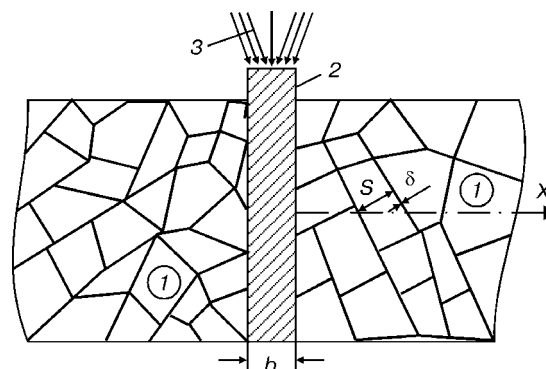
Схема сварки встык плавлением пористого материала со сплошной расплавленной прослойкой: 1 — основной материал; 2 — прослойка; 3 — тепловой поток
